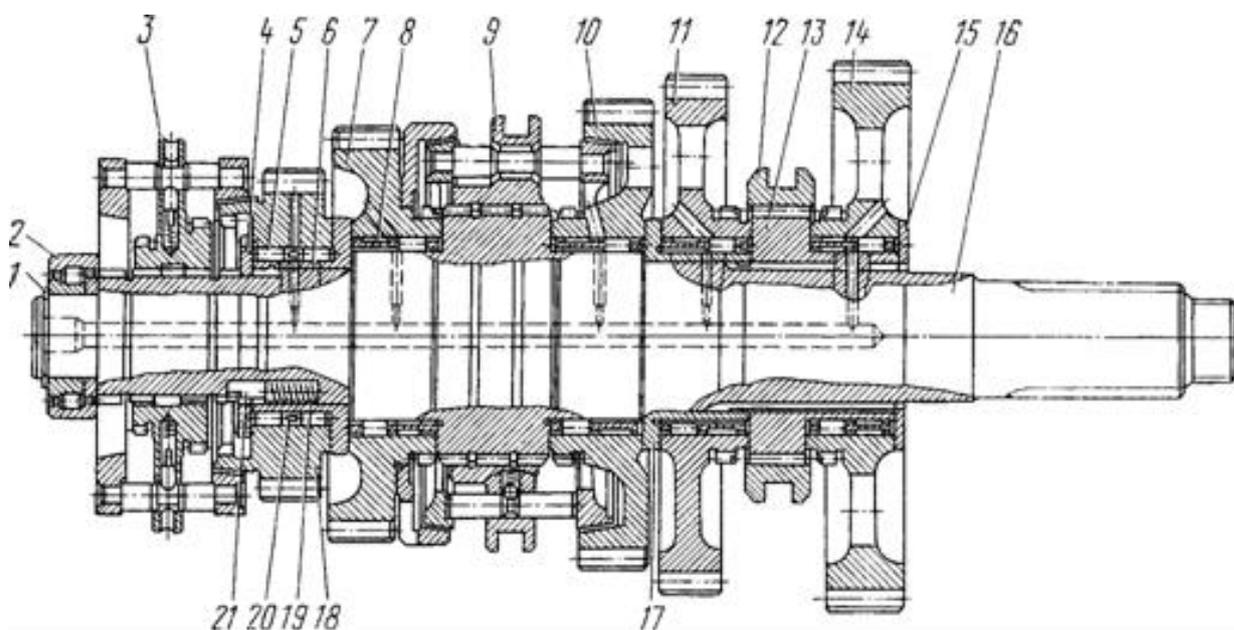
Ведомый вал в сборе: 1 – кольцо стопорное; 2 – подшипник передний роликовый; 3 – синхронизатор IV и V передач; 4 – кольцо упорное; 5 – ролики подшипника IV передачи; 6 – втулка шестерни IV передачи; 7 – шестерня III передачи; 8 – подшипник роликовый; 9 – синхронизатор II и III передач; 10 – шестерня II передачи; 11 – шестерня заднего хода; 12 – муфта включения I передачи и заднего хода; 13 – втулка шестерни I передачи; 14 – шестерня I передачи; 15 – шайба упорная; 16 – вал ведомый; 17 – втулка шестерни заднего хода; 18 – шестерня IV передачи; 19 – пружина; 20 – втулка промежуточная; 21 – шпонка замковая
